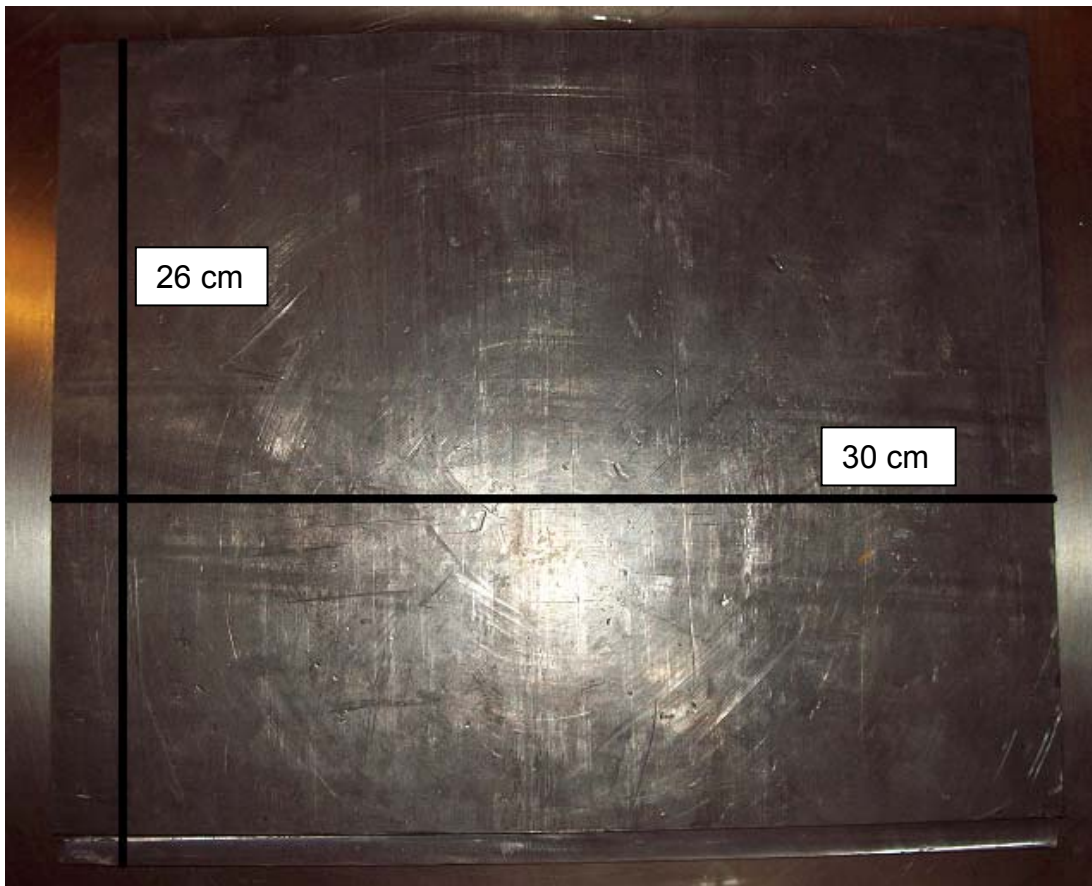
Placa de chumbo construída com as dimensões de comprimento e largura.
